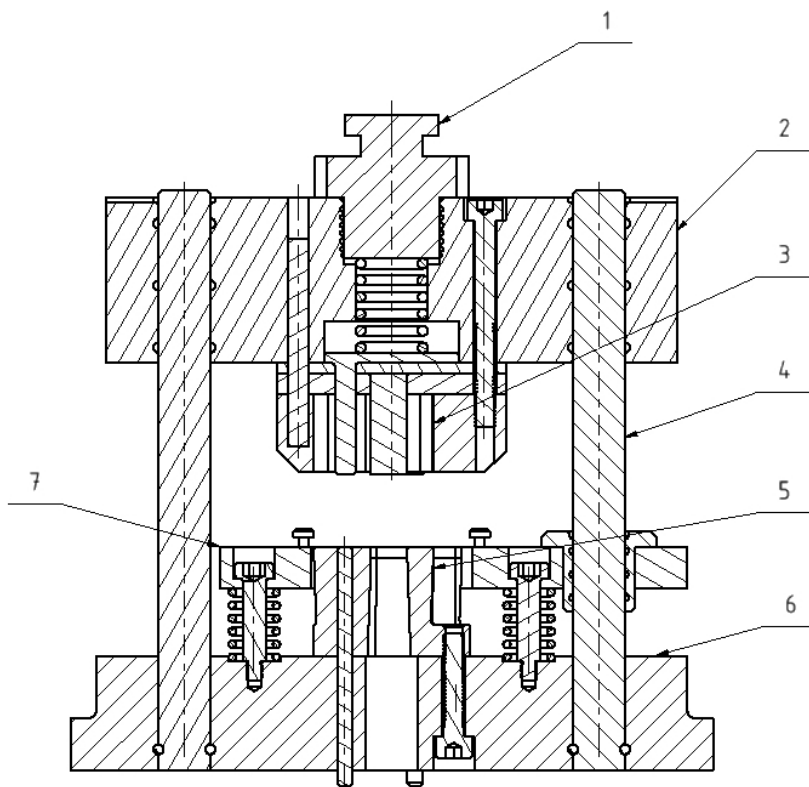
Ausstanzwerkzeug Komplettschnitt für Stern
